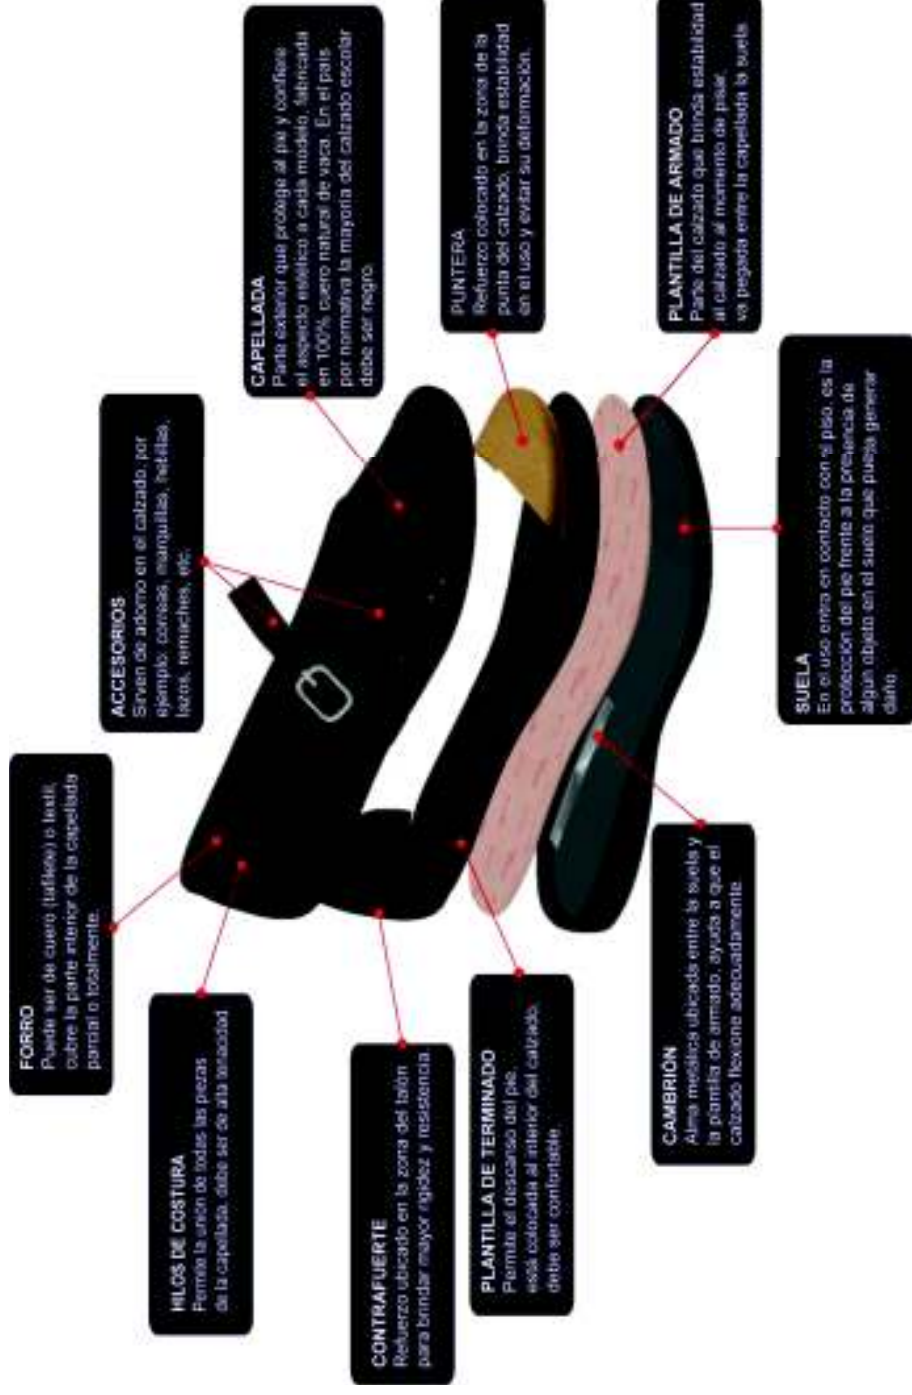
Plano de ingeniería calzado escolar femenino de cuero
